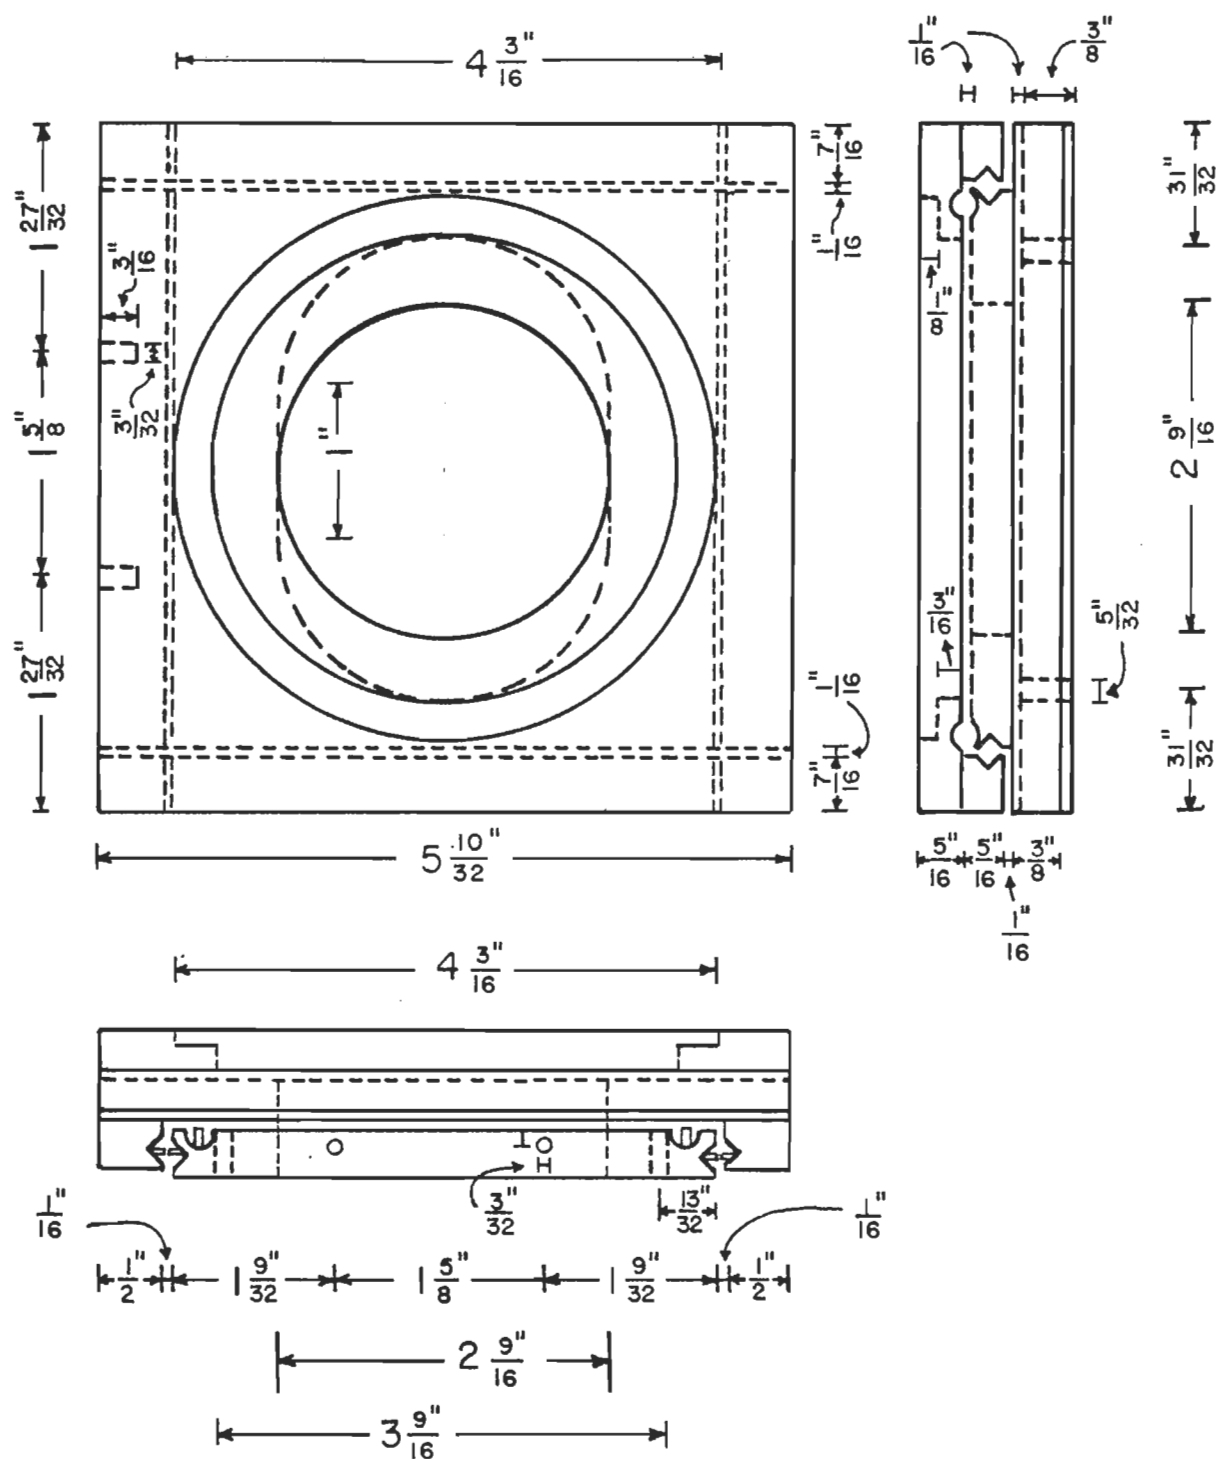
Plan détaillé de la section c vue dans un plan horizontal supérieur et dans deux plans verticaux.
